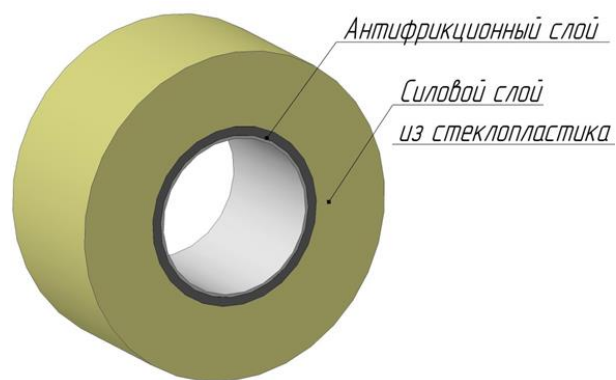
Общий вид подшипника скольжения из композиционно-волокнистых материалов
